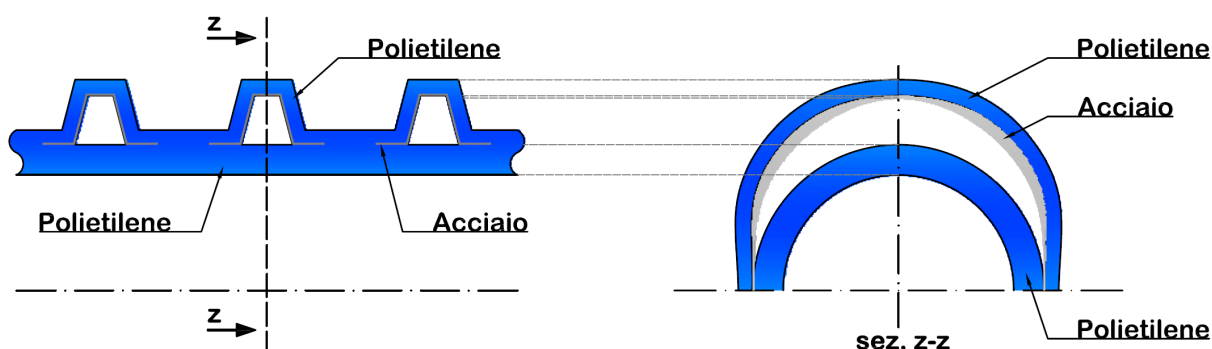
Sezione del tubo PALADEX spiralato rinforzato con acciaio.
